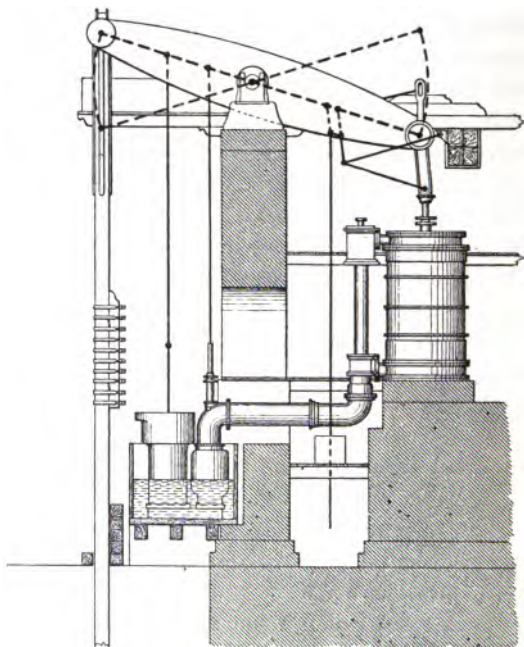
Machine de Cornouailles, pour l'épuisement des mines.
